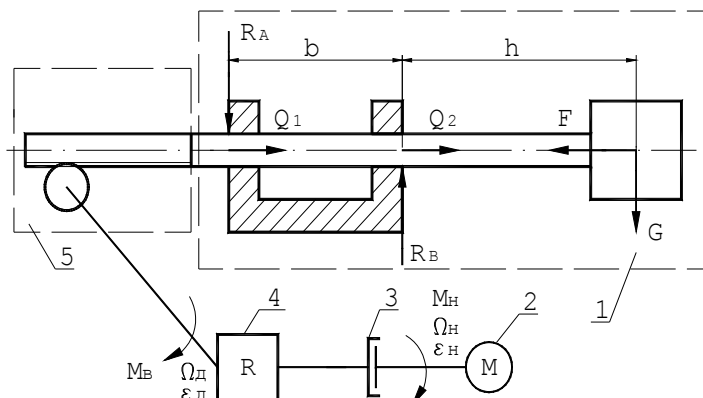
Кинематическая схема звена подвижности ПР: 1 – исполнительный механизм (конструкция руки робота и направляющих звена подвижности); 2 – исполнительный двигатель; 3 – муфта; 4 – редуктор; 5 – реечная пара
